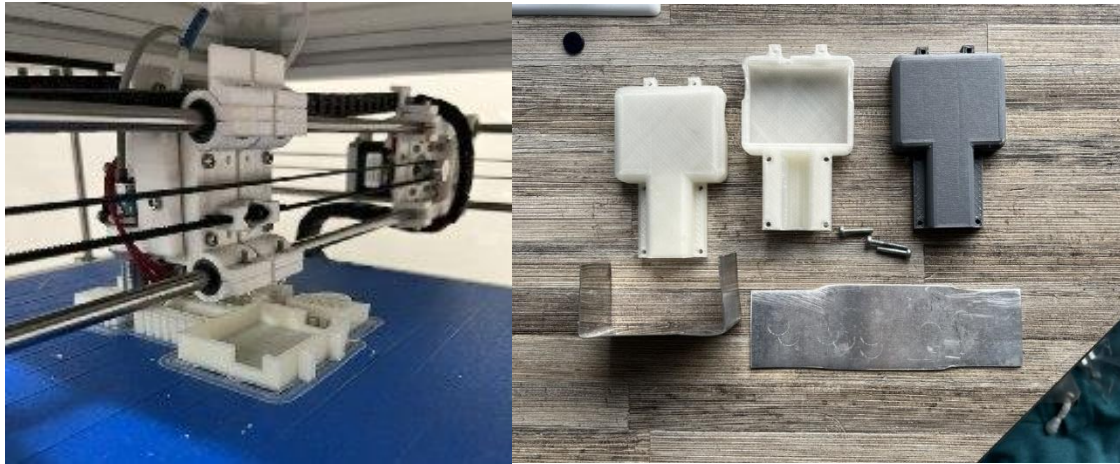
Fabricación de piezas complementarias del sistema VTOL mediante impresión 3D.
